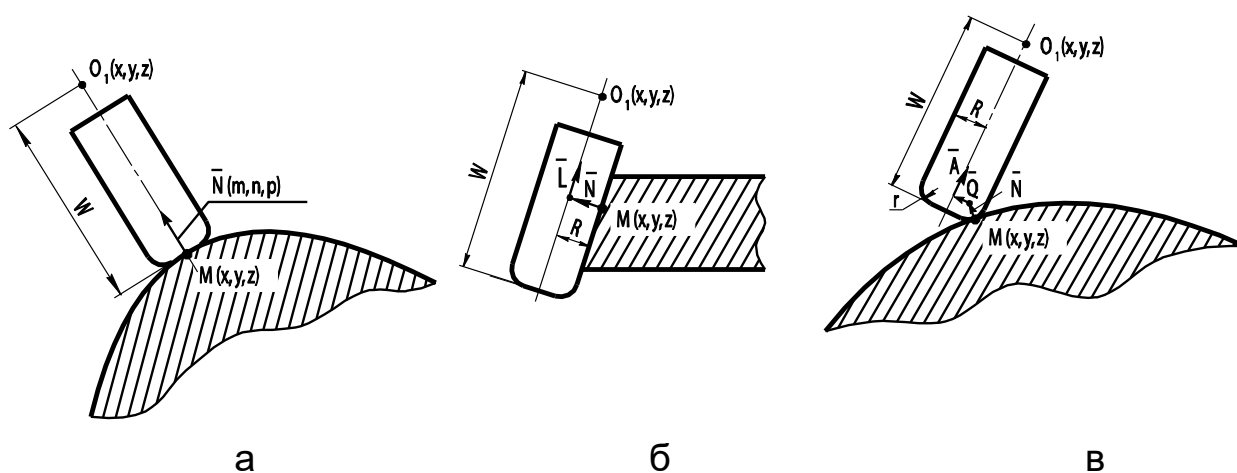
Основные виды пятикоординатного фрезерования:
